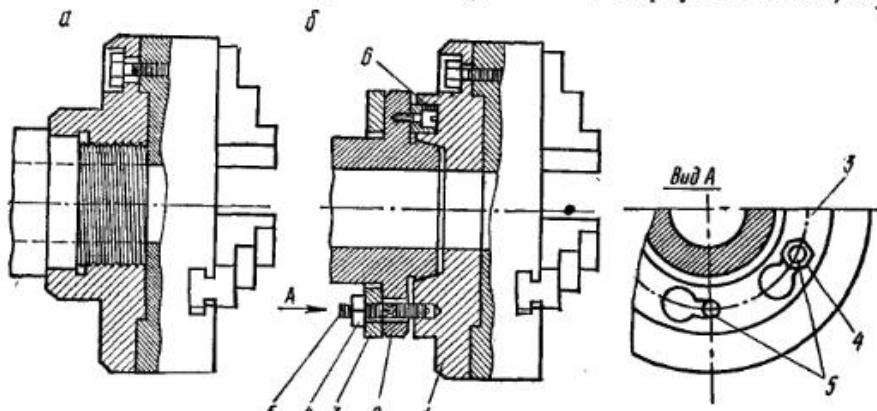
Установка токарного патрона на резьбовом конце шпинделя (а) и фланцевом (б)
